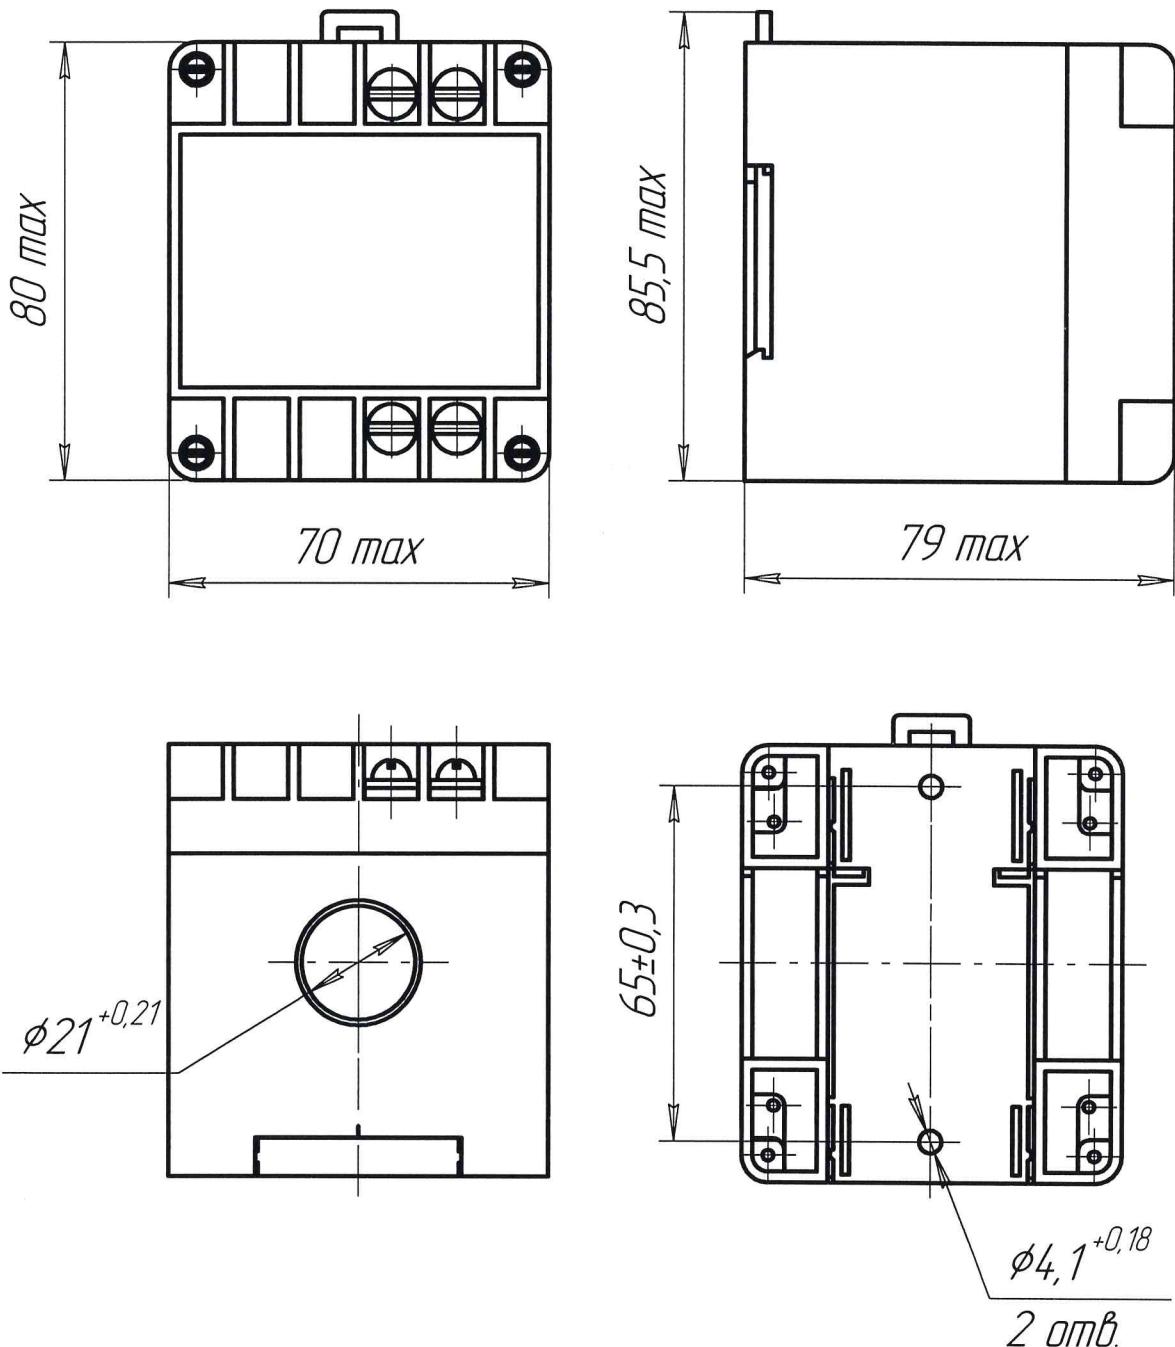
Габаритные, установочные размеры преобразователей
